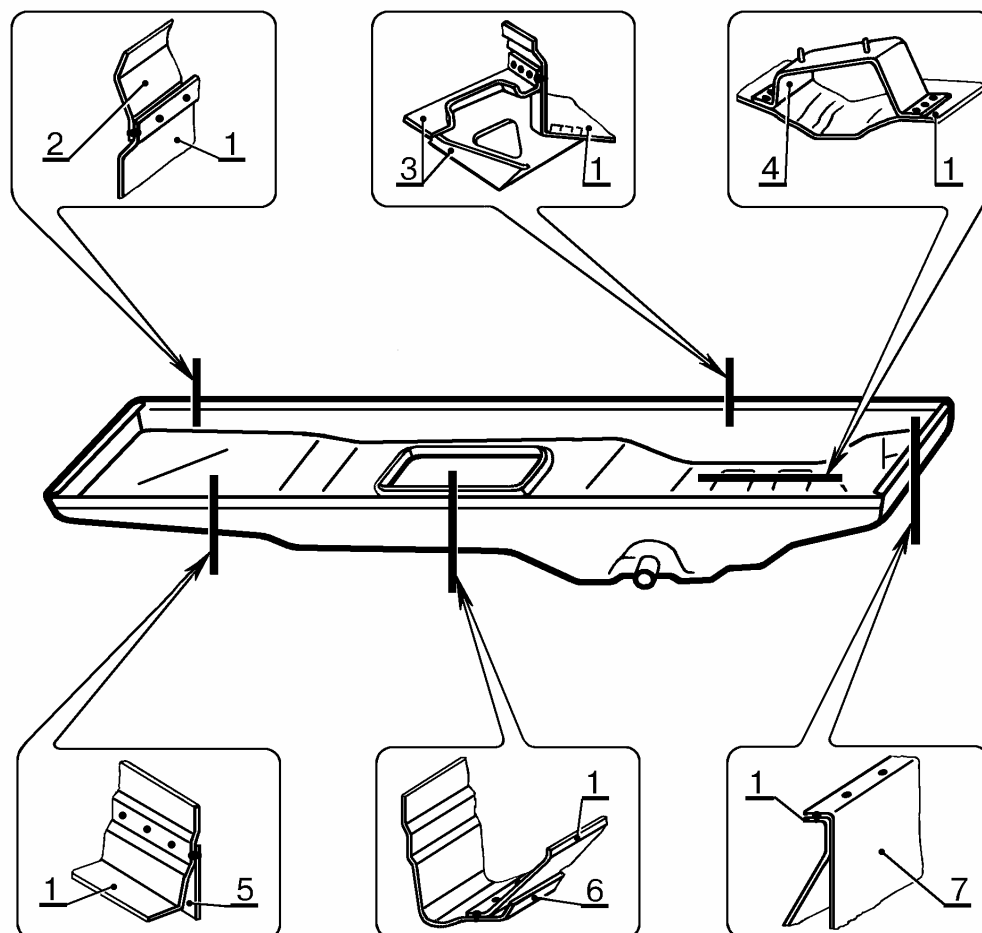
Соединение коробки воздухопритока с сопрягаемыми деталями
